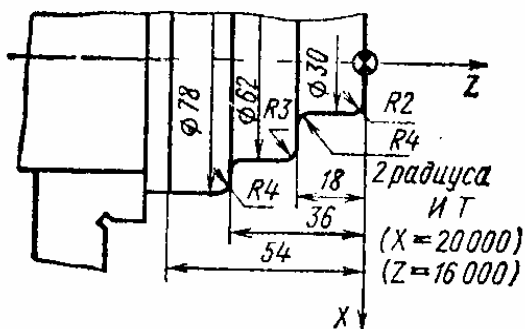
Эскиз заготовки (к задаче 16.11)
